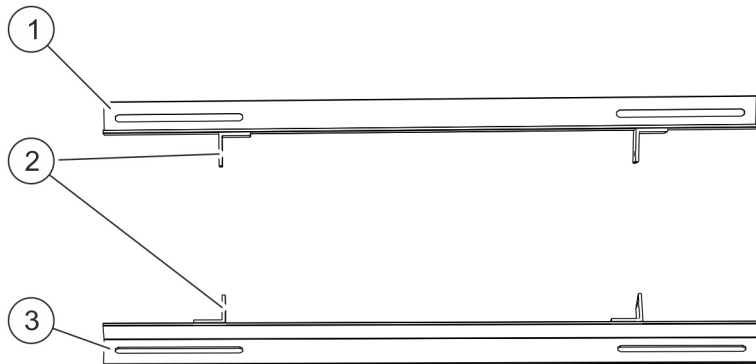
Befestigung für Gewichtsführung im Tunnel
